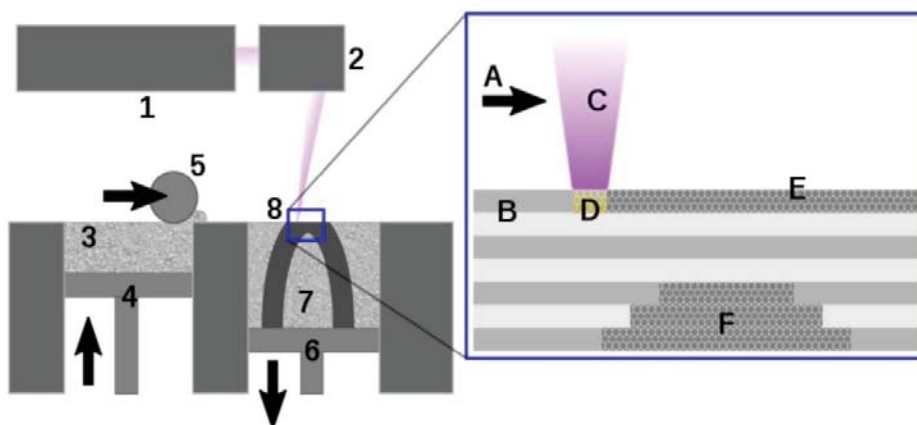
Procedetul de printare 3D prin sinterizare selectivă
